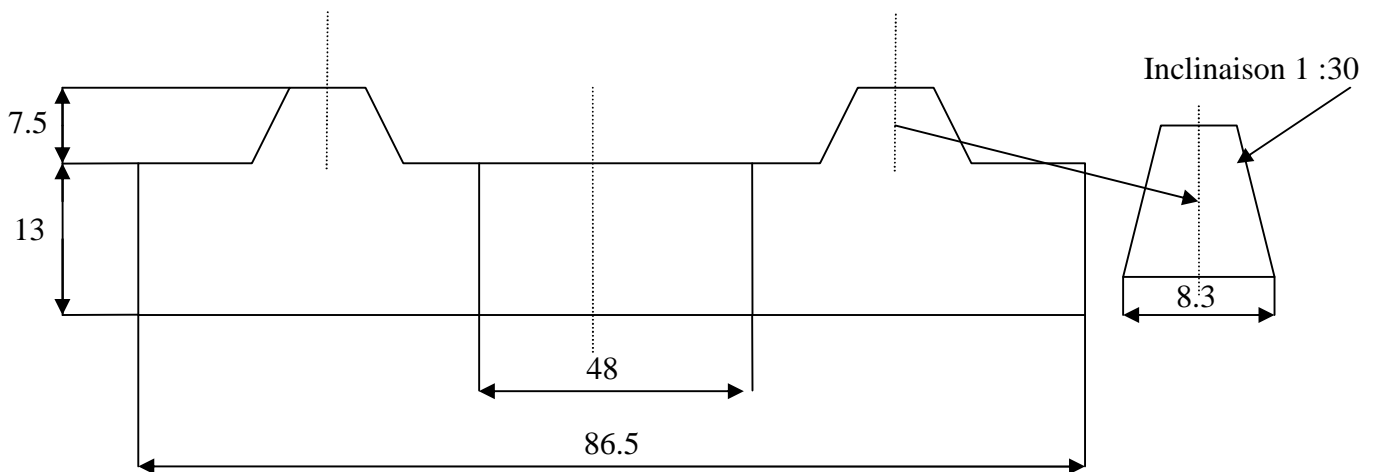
Forme et dimensions de l'anneau de court circuit
